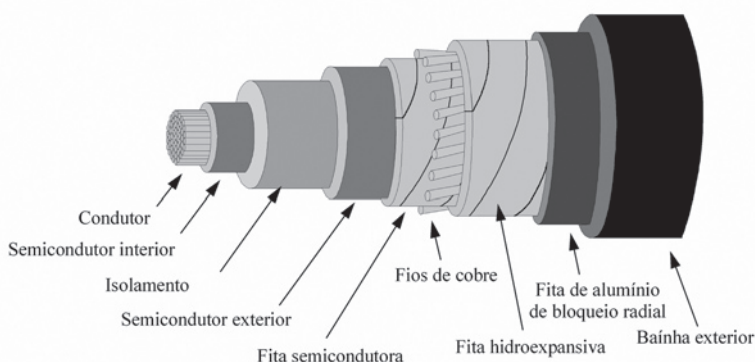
Cabo de 60kV com isolamento em XLPE e blindagem por fios de cobre.
